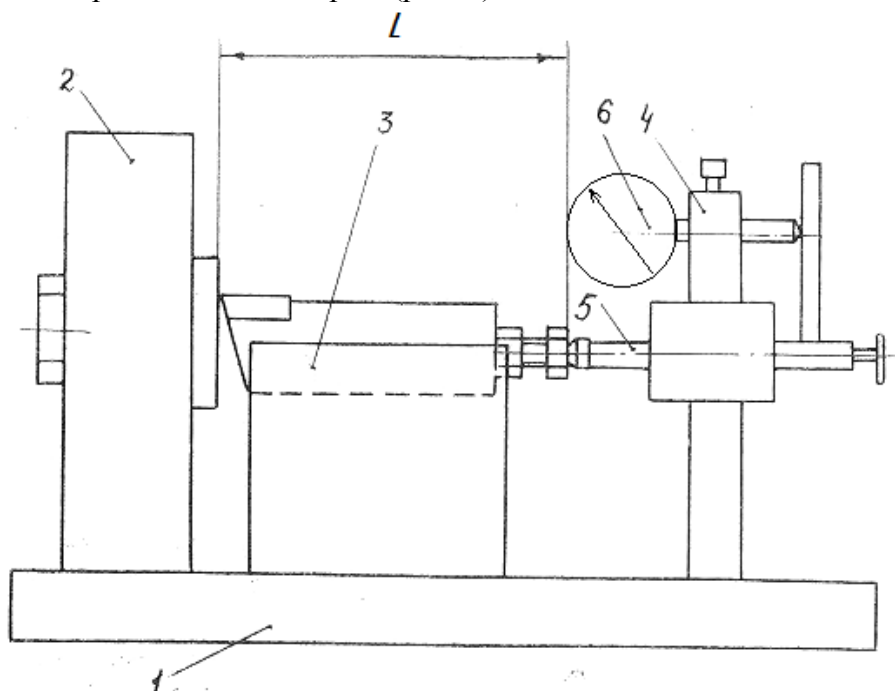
Схема приспособления для размерной настройки резцов вне станка
